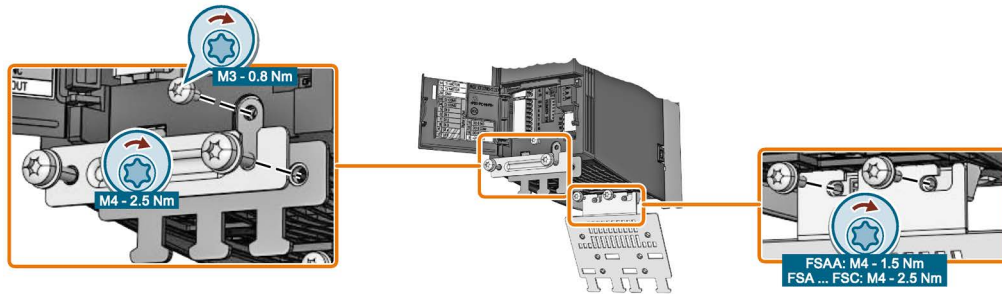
Schirmbleche montieren am Beispiel eines Umrichters Frame Size A
